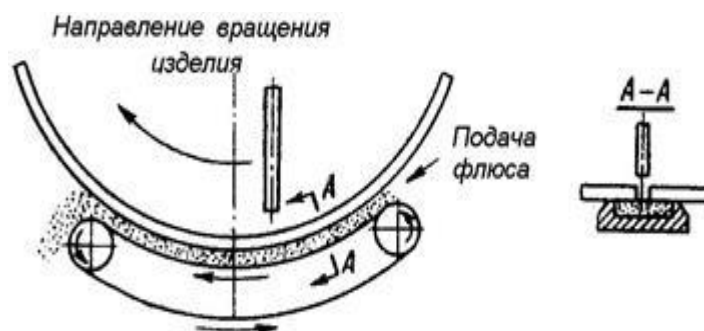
Флюсоремінна подушка для зварювання кільцевих швів
